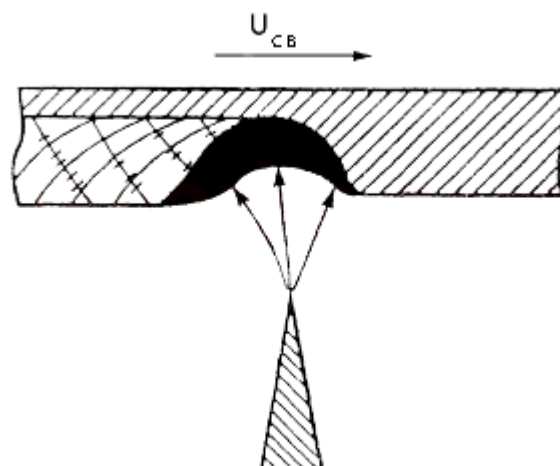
Формирование ванны и шва при ручной дуговой сварке в потолочном положении
